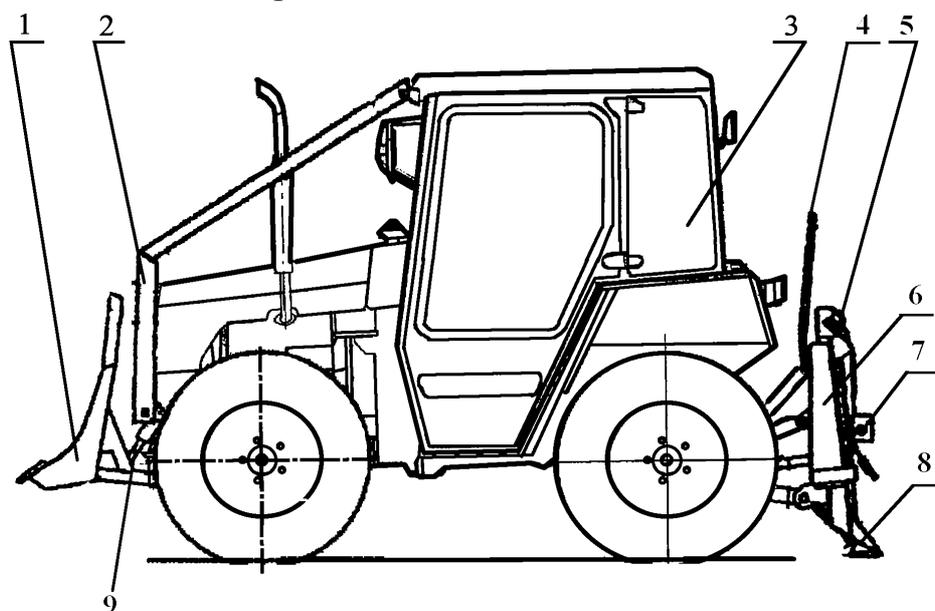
Малогабаритная трелевочная машина МТЗ-320ТТ: 1 – отвал-торцеватель; 2 – ограждение; 3 – кабина; 4 – ограждение трелевочного приспособления; 5 – верхний канатонаправляющий блок; 6 – упорный щит; 7 – нижний канатонаправляющий блок; 8 – упор; 9 – гидроцилиндр
